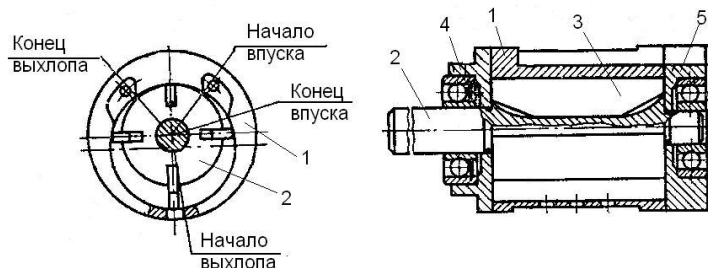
Схема пластинчатого ПМ. 1- статор, 2- ротор, 3 – пластины, 4 и 5 – передняя и задняя крышки
